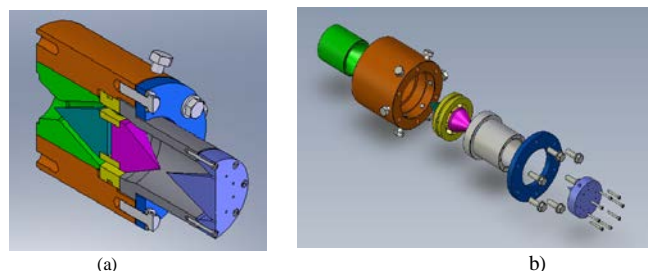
Diseño de cabezal de extrusión: (a) vista de corte y (b) modelo explosionado del ensamble.
